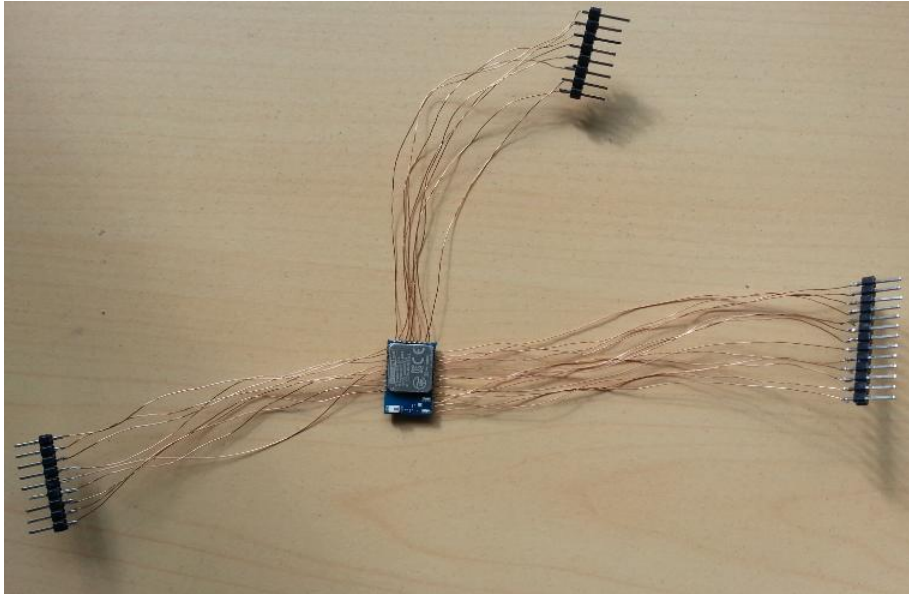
Face avant du module Bluegiga BLE112 soudé
